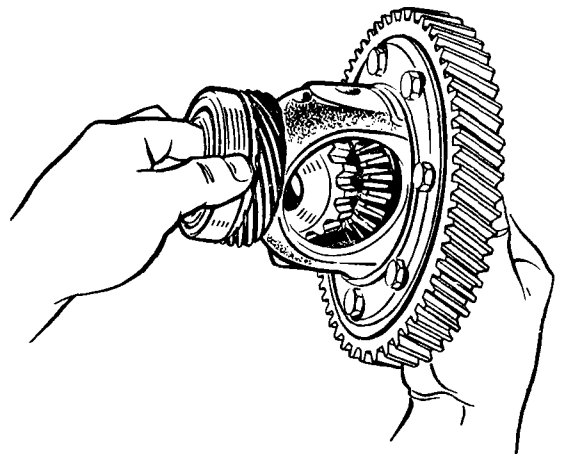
Выкатывание шестерен полуоси из коробки дифференциала
